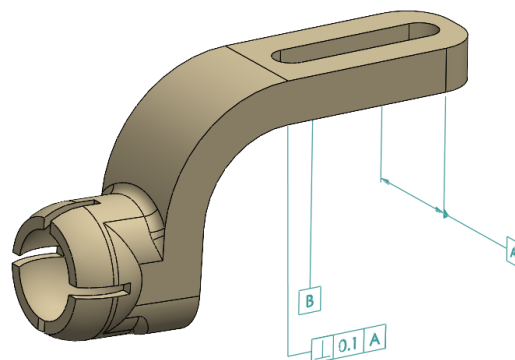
Tolerancias geométricas “Extensión muñeca-pulgar”
